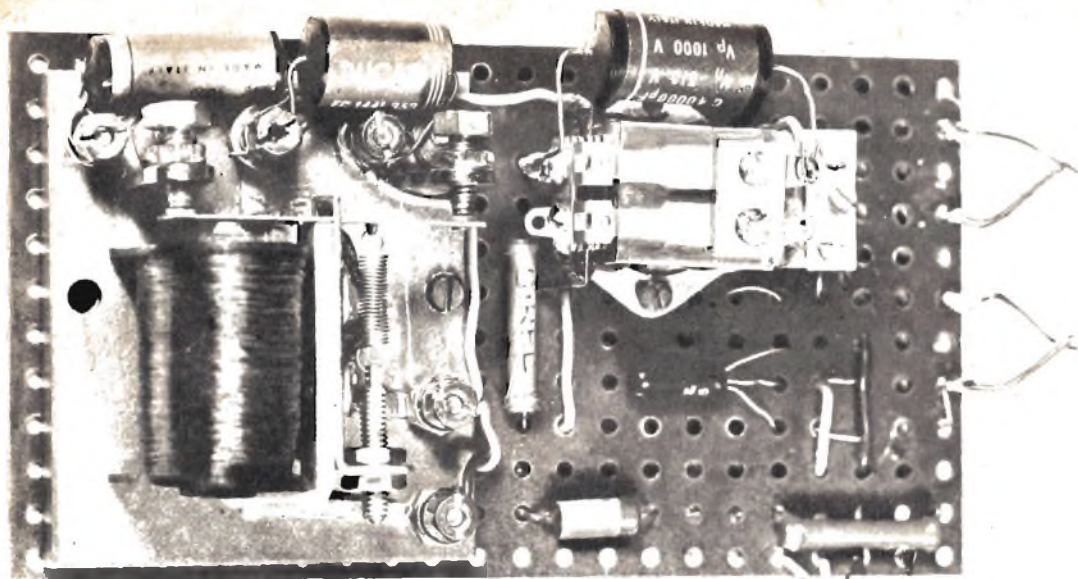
Da questa vista in pianta della basetta si rileva la esatta disposizione di tutti i componenti.
